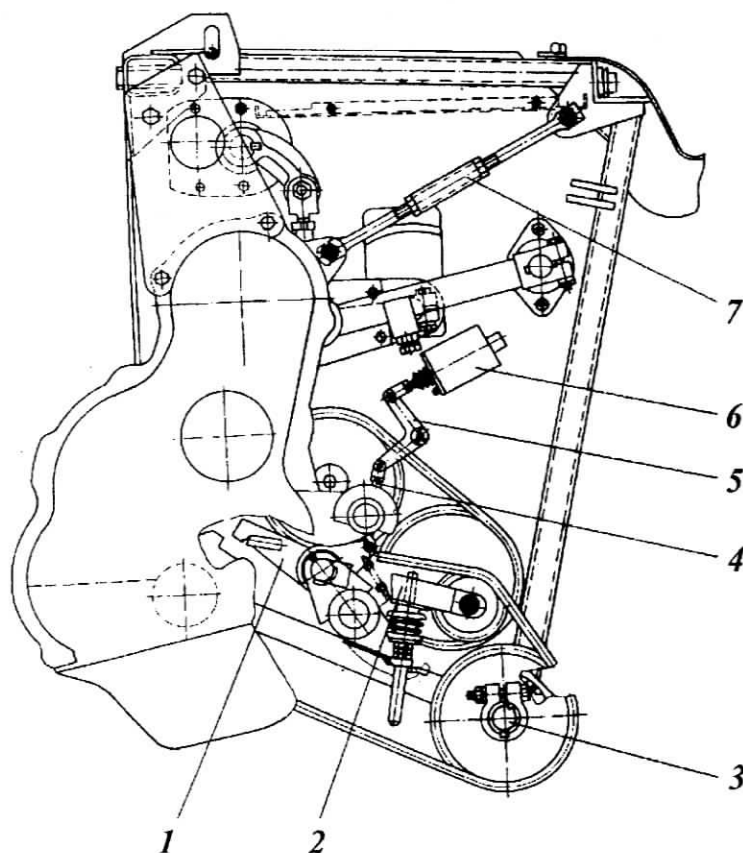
Питающий аппарат. Механизм привода жатки с муфтой останова.
